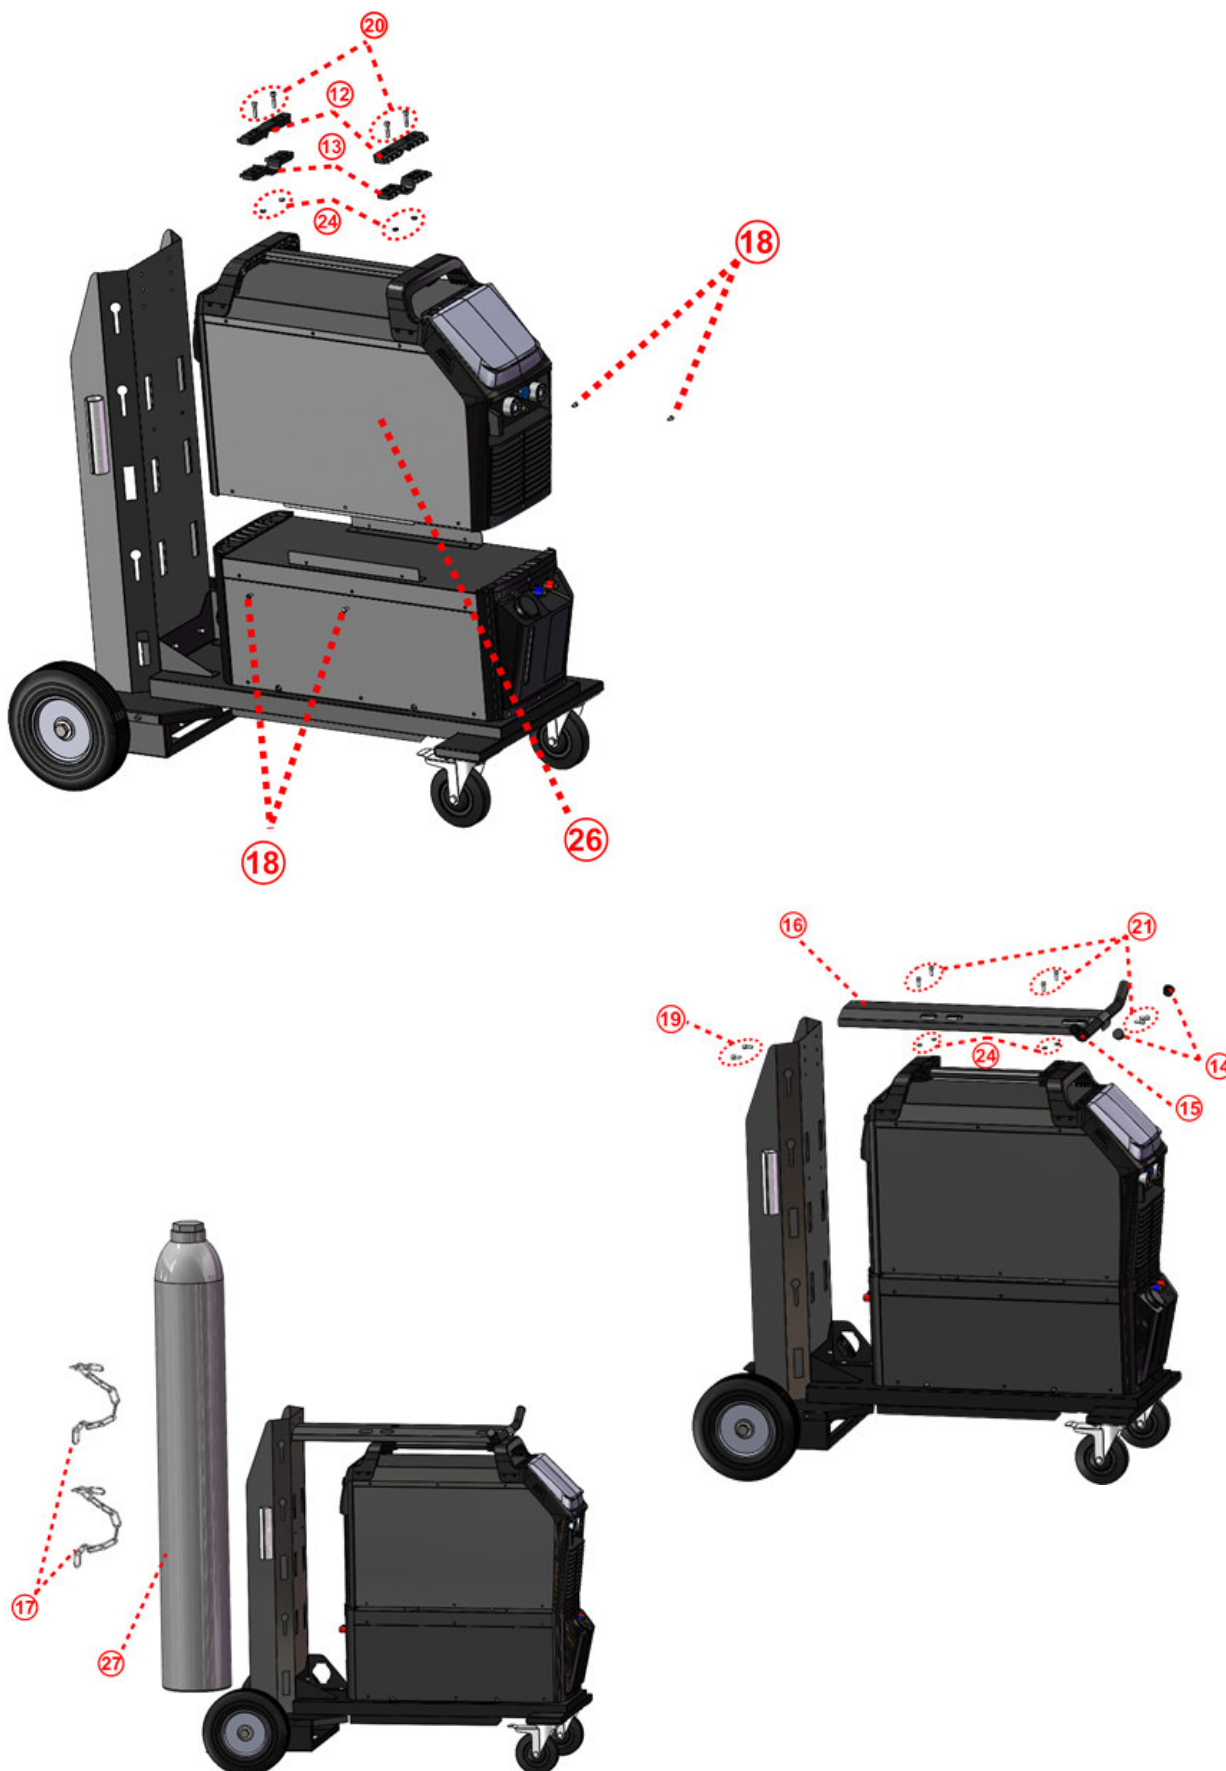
Montage des Schweißgerätwagens 5, 6 & 7
